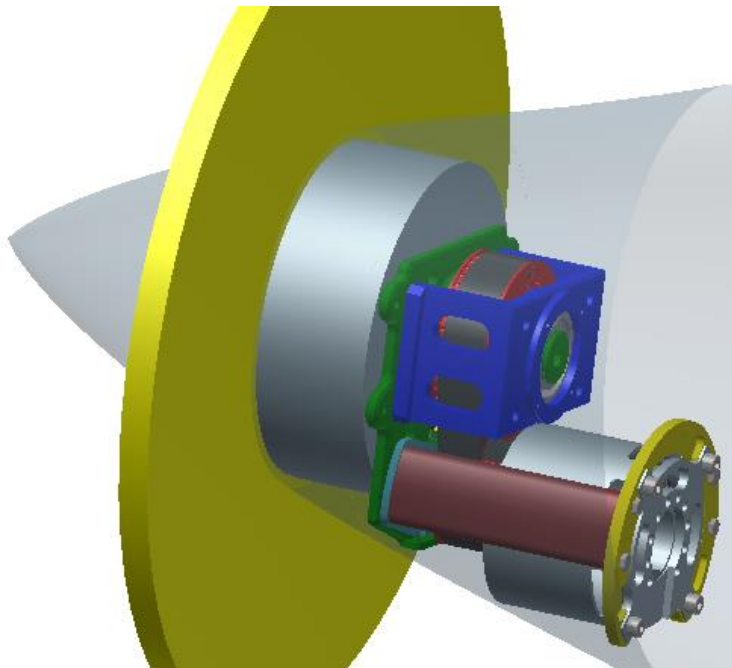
Varianta reduktoru s napínací kladkou - zdroj autor
